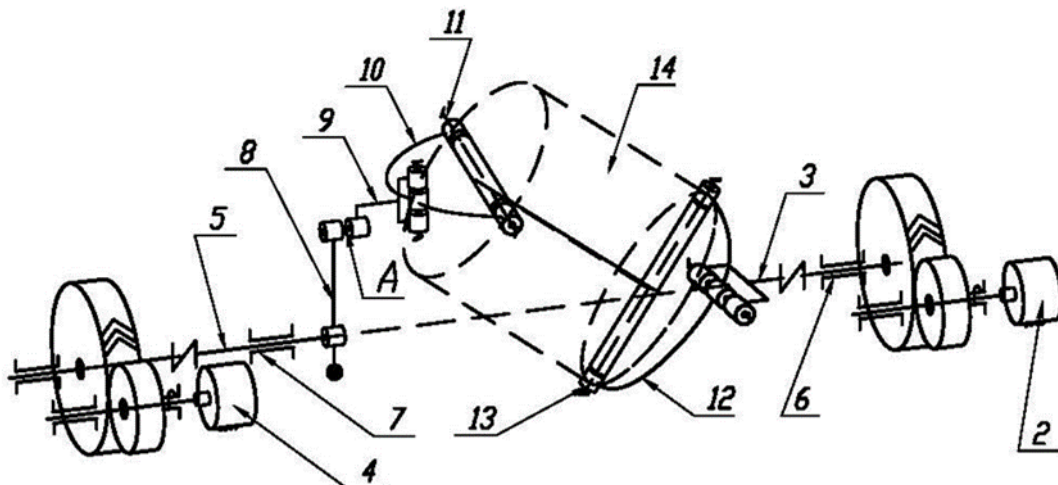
Кінематична схема машини нової конструкції для обробки деталей
